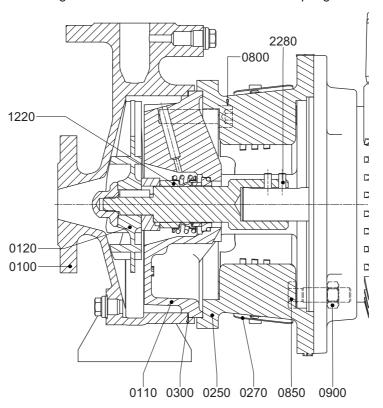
Montage der Steckwelle für Pumpengröße 25-...
